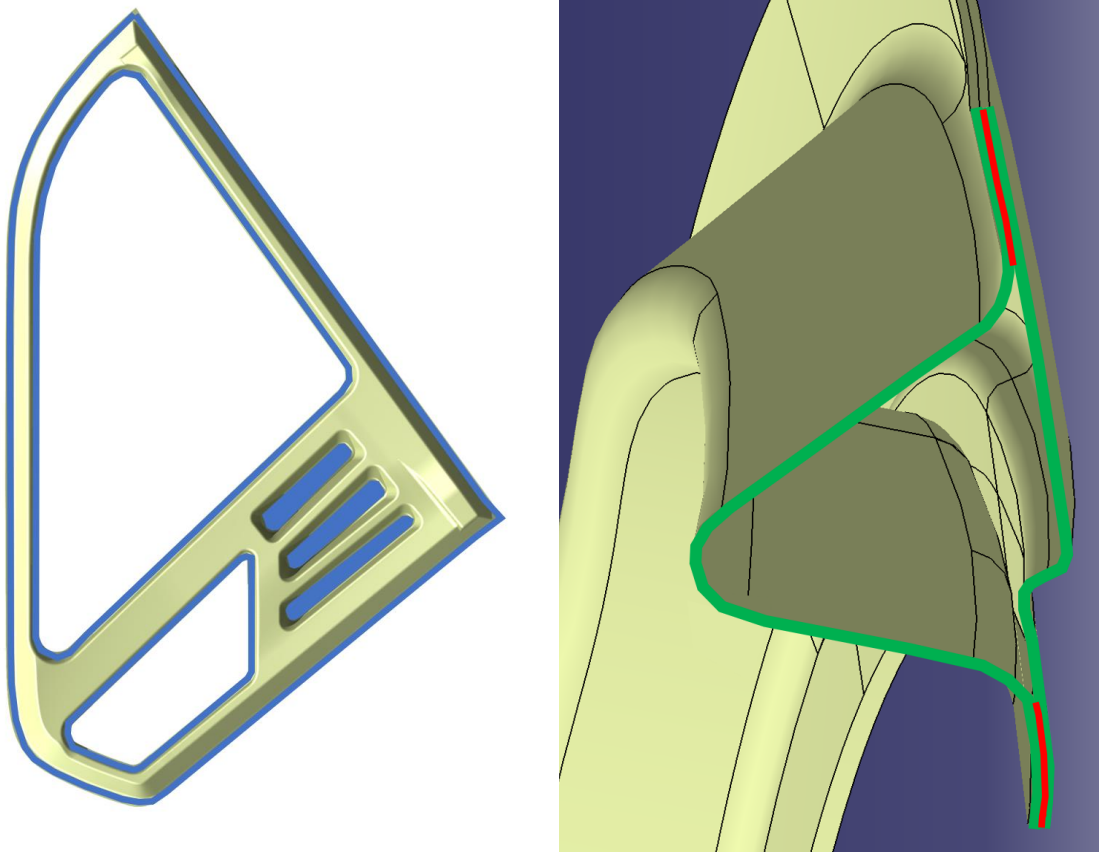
Hubschraubertür innenseitig, mit blauer Kennzeichnung der Bereiche der Fügezonen (links) und Flansch-Ausprägung zur Erzeugung einer flächigen Anbindung zwischen Innen- und Außenschale (rechts)
